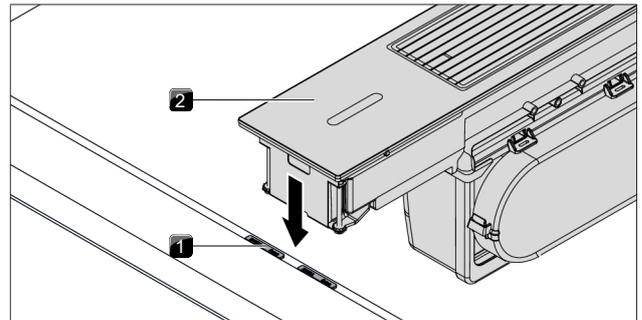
Höhenausgleichsplatten bei flächenbündiger Montage
